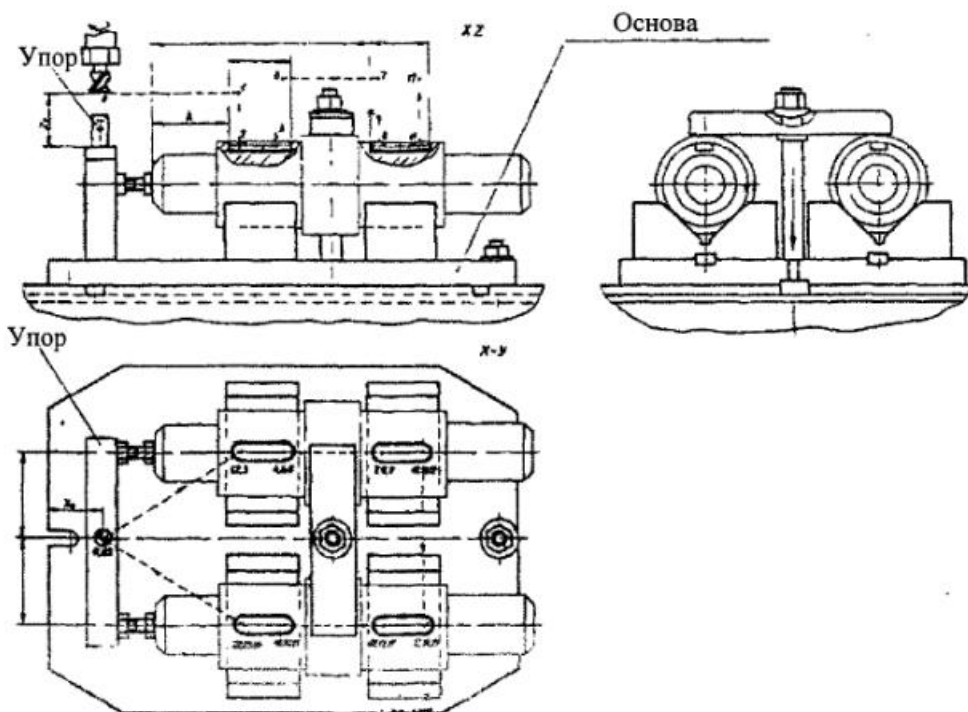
Фрезерування шпонкових пазів на верстаті з ЧПК.
